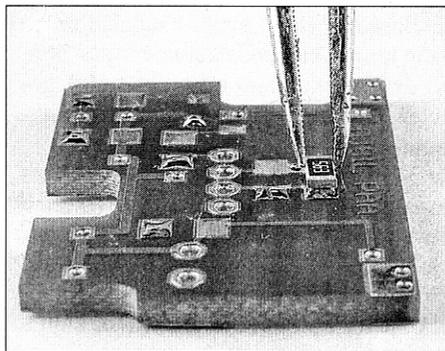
Die Positionierung des Bauelementes erfolgt am besten mit einer Pinzette.
